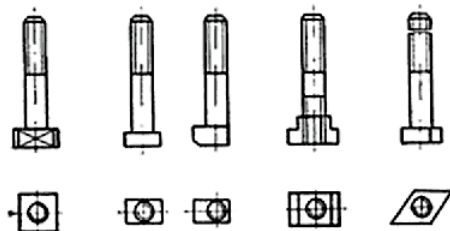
Станочные болты и шпильки для крепления заготовок
